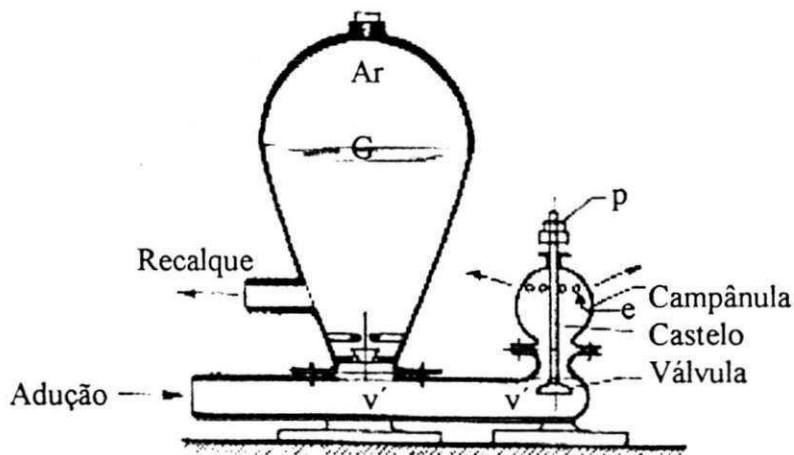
Corte de uma elevadora tipo carneiro hidráulico. Fonte: Macintyre (1983)
